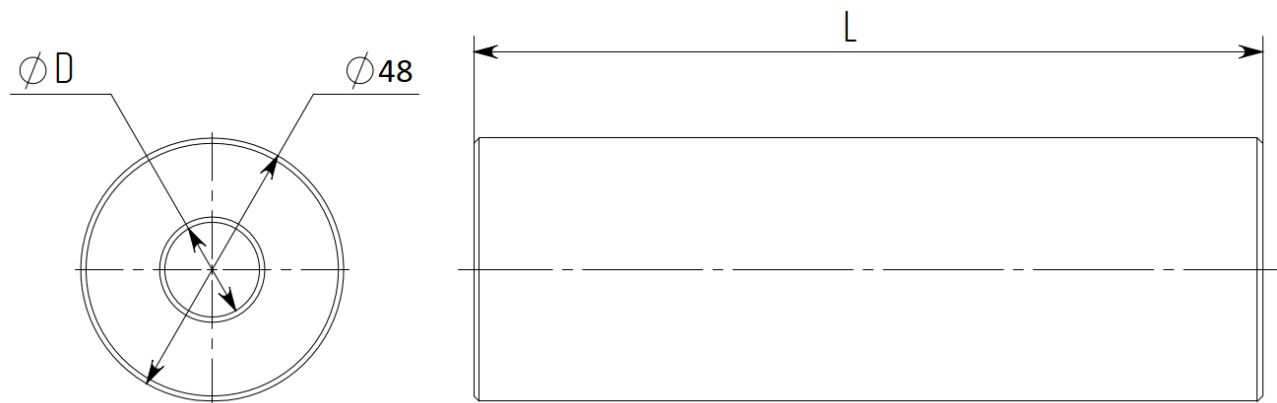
Габаритные и установочные размеры поплавка из сферопластика, полипропилена или полиэтилена
